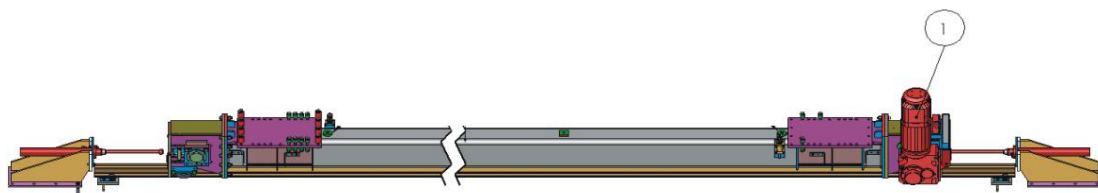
Momentos provocados por extensión de horquillas en eje débil
